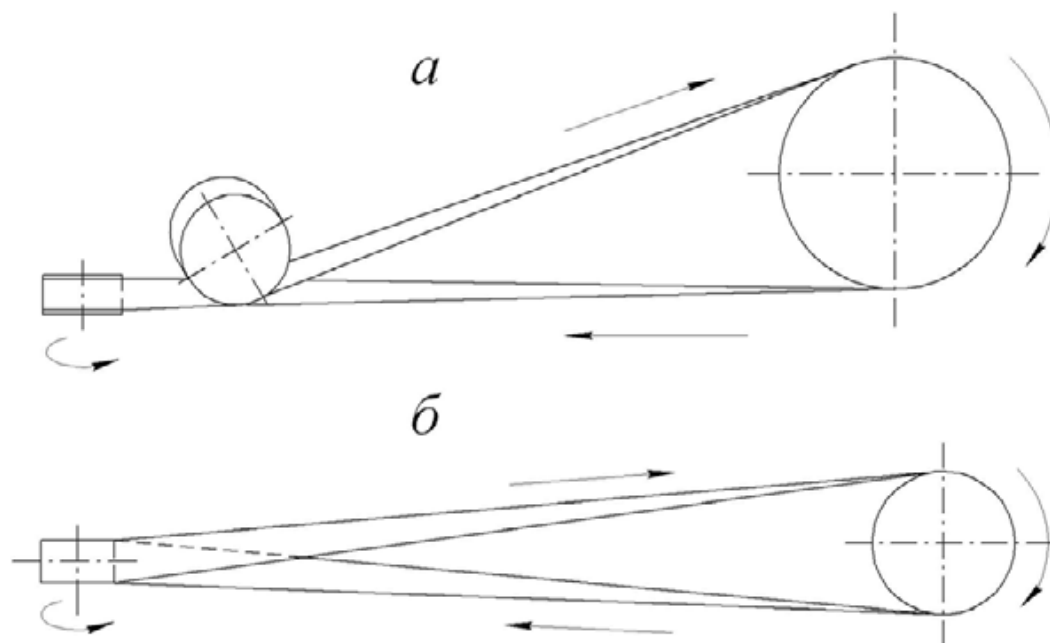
Полуперекрестная поликлиновая передача: а – с натяжным роликом; б – без натяжного ролика
